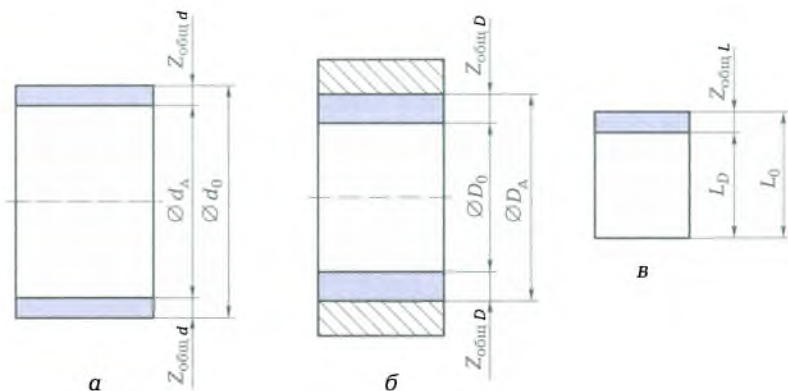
Схемы определения общего припуска на обработку наружной (а), внутренней (б) цилиндрической и плоской (в) поверхностей
